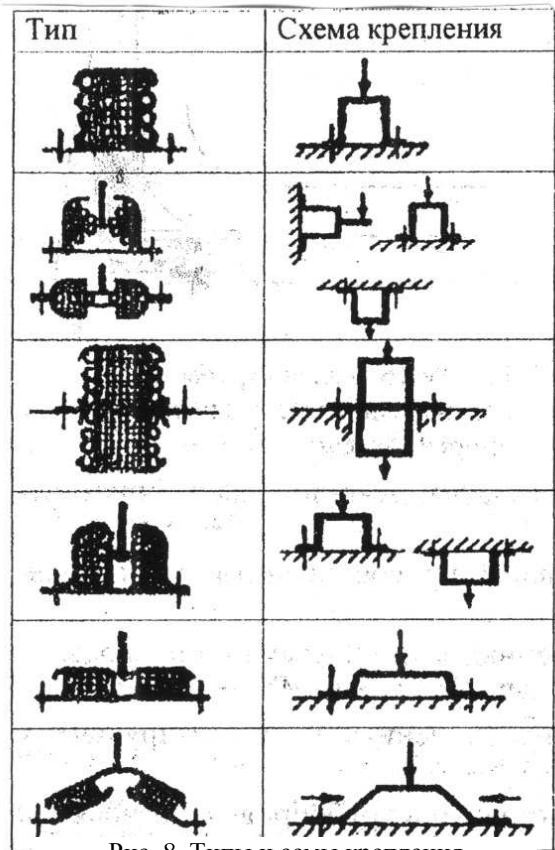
Типы и схемы крепления металлочных амортизаторов
